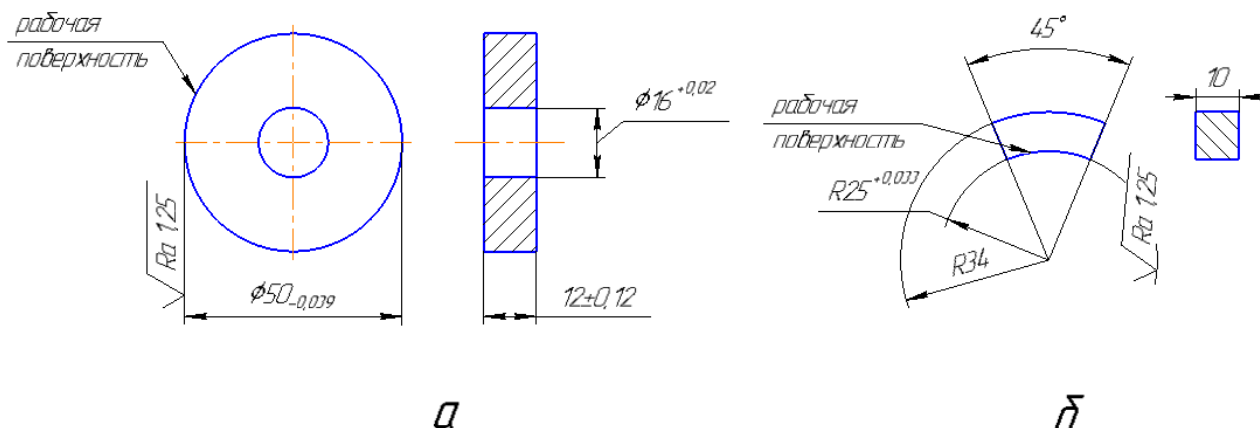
Размеры образцов и требования к шероховатости поверхности, а - диск, б – колодка
